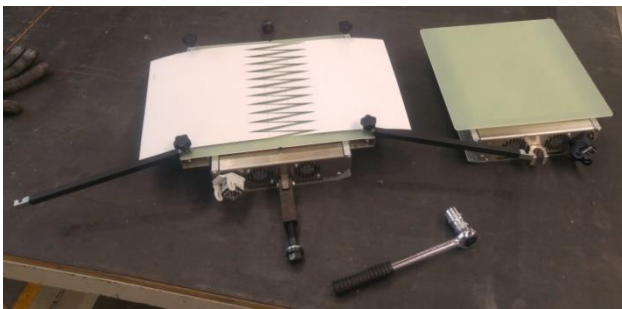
Positionnement de la bande Fabric sur la plaque de jonction
